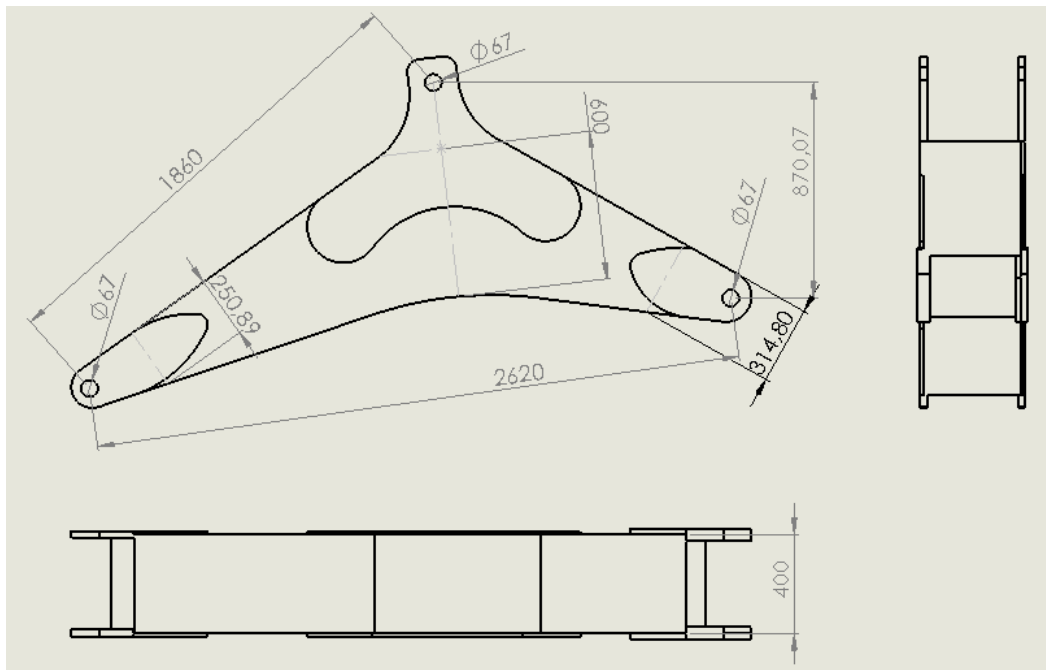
Plano de tres vistas generado en SolidWorks de la pluma.
